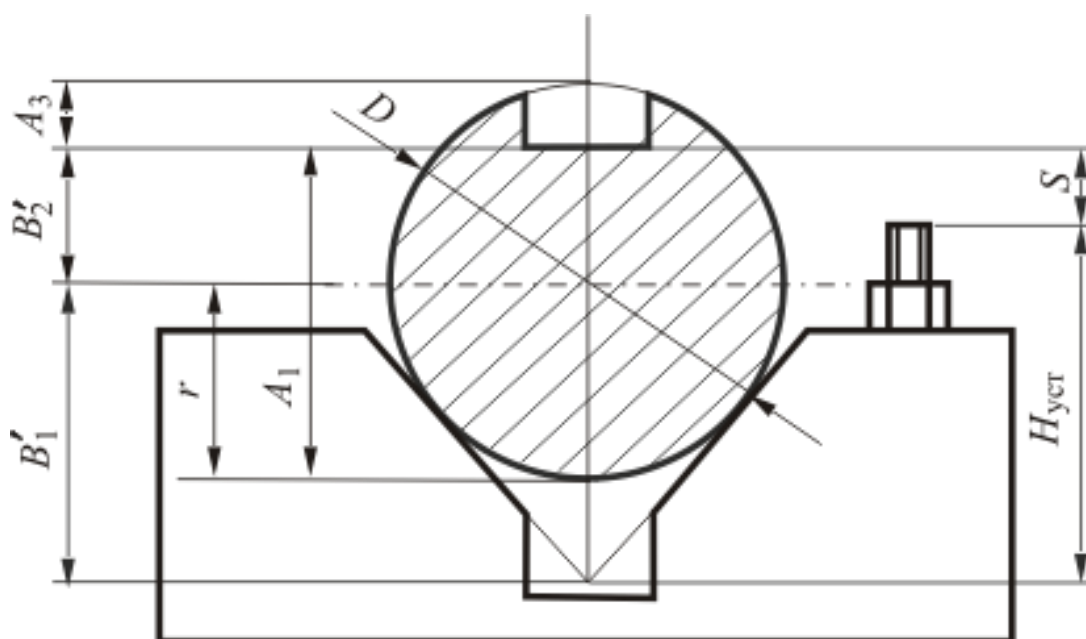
Схема настройки инструмента при обработке заготовки в размер $A_3 = 5^{+0,2}$
